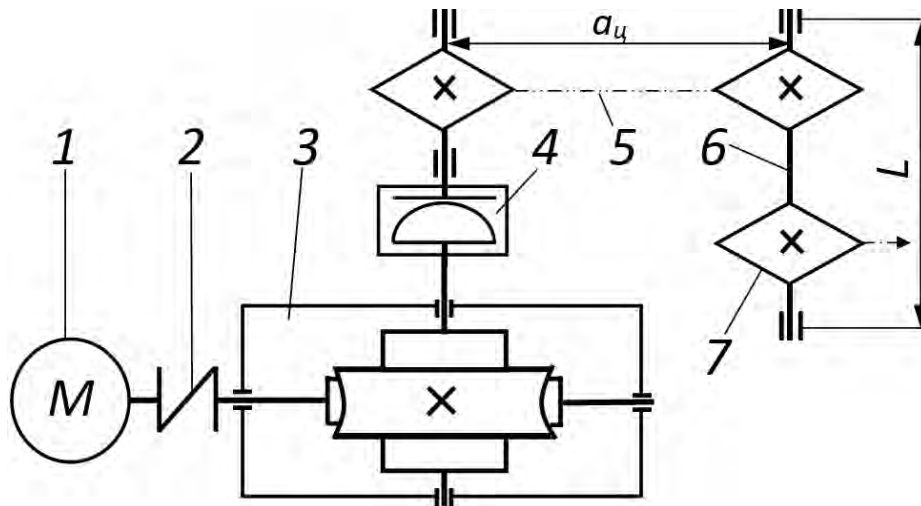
Схема привода скребкового конвейера (вид сверху): 1 – асинхронный электродвигатель; 2 – муфта упругая втулочно-пальцевая; 3 – редуктор червячный (с нижним расположением червяка); 4 – муфта кулачково-дисковая; 5 – цепная передача; 6 – приводной вал; 7 – приводная звездочка
